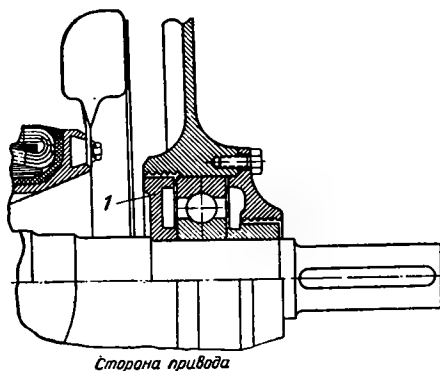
Подшипниковый узел с шарикоподшипником.
